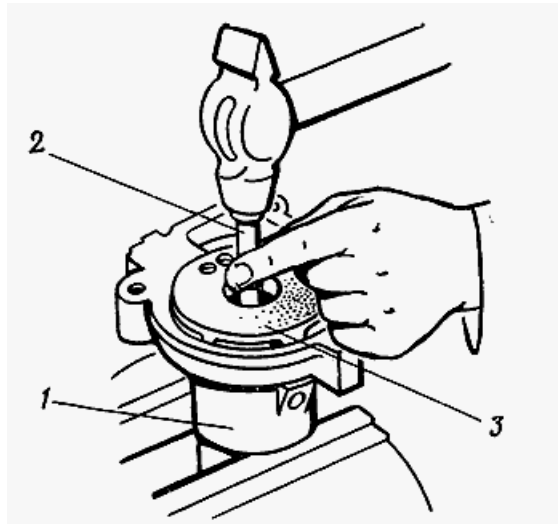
Випресування валика водяного насосу 1— корпус водяного насосу; 2 — виколотка; 3 — крильчатка
